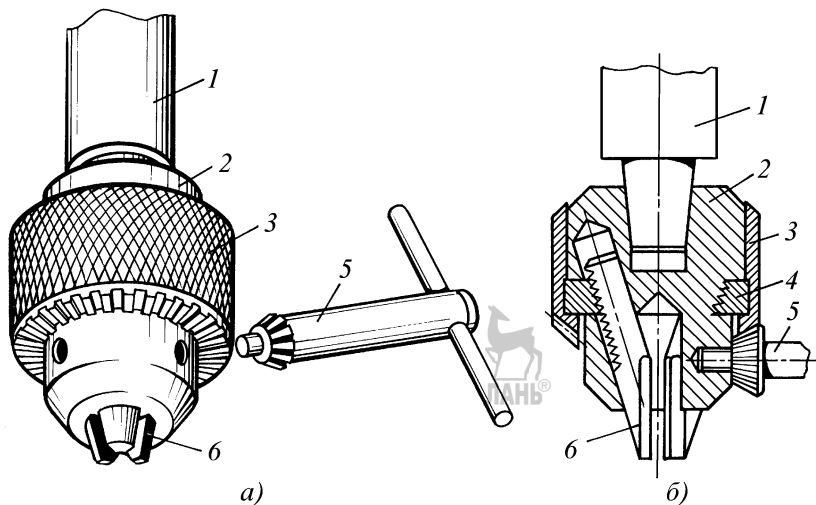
Общий вид (а) и схема (б) сверлильного трехкулачкового патрона
